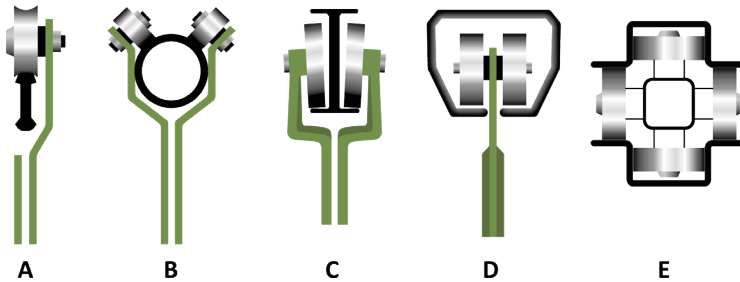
Diferentes diseños de contactos carril de rodadura/carro unido a la cadena: (A) carro montado sobre un carril de rodadura en forma de doble T con un único punto de apoyo; (B) carro montado sobre un carril tubular con dos puntos de apoyo; (C) carro suspendido del ala inferior de un carril de rodadura en forma de doble T; (D) configuración con carril de rodadura que envuelve al carro, que apoya en el ala inferior del carril, configuración óptima para realizar trayectorias con cambios de pendiente vertical; (E) carril de rodadura que envuelve al carro que discurre por dentro del mismo y presenta cuatro puntos de apoyo, configuración óptima para realizar trayectorias con cambios de pendiente vertical y horizontal. Extraído y adaptado de Lindkvist, R.G.T. (1985). *Handbook of Materials Handling*. Ellis Horwood Ltd. England.
